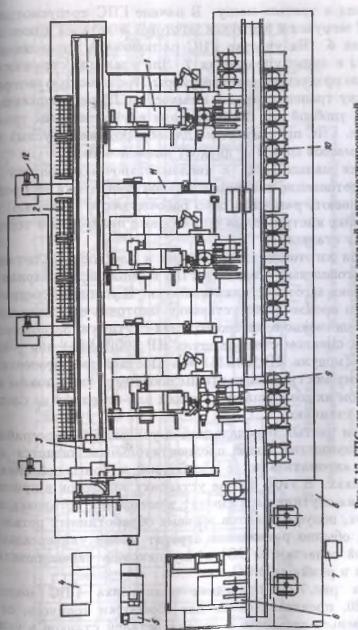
ГПС для изготовления корпусных деталей с автоматизирован системой инструментообеспечения и уборыя струмых
